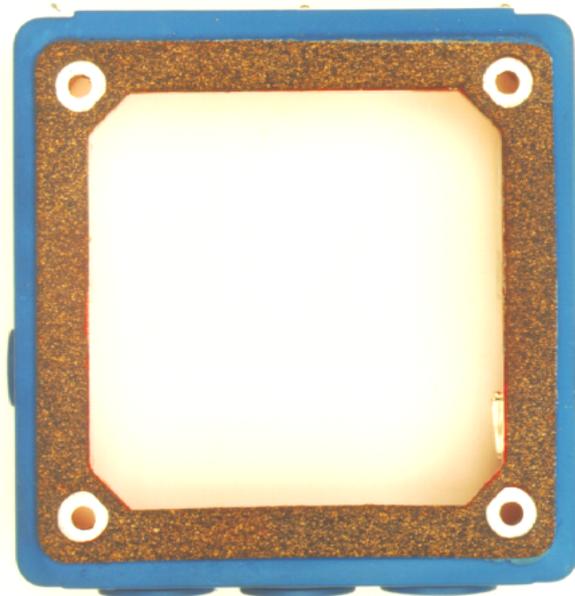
Abdichtung zwischen Ständergehäuse und Klemmenkasten mit
